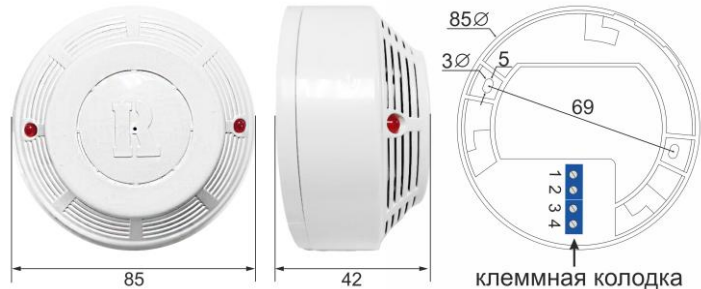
Внешний вид, габаритные и установочные размеры извещателя
